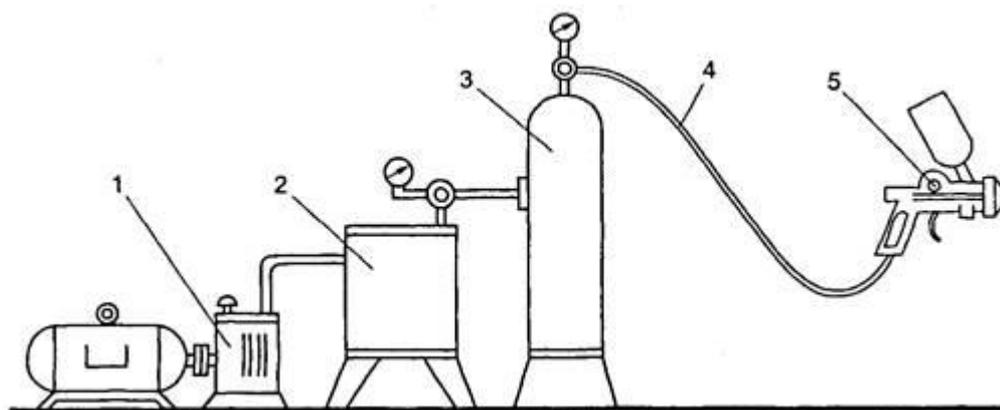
Схема установки для пневматического распыления: 1 — компрессор; 2 — масловлагоотделитель; 3 — ресивер; 4 — гибкий шланг; 5 — краскораспылитель
